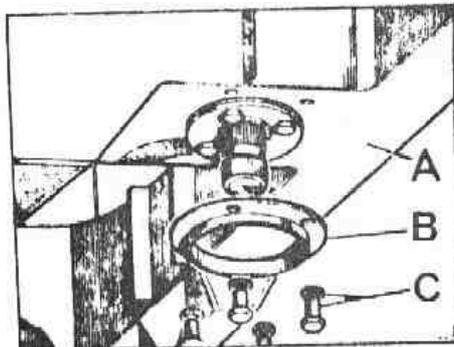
Placa-brida para el montaje de la caja compensadora
